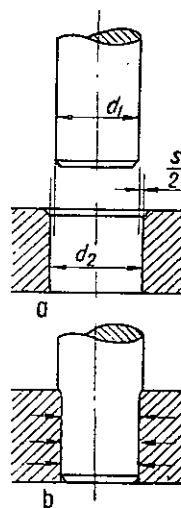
Asamblarea prin încălzirea piesei cuprinzătoare: a — piesele înainte de asamblare; b — piesele asamblate
